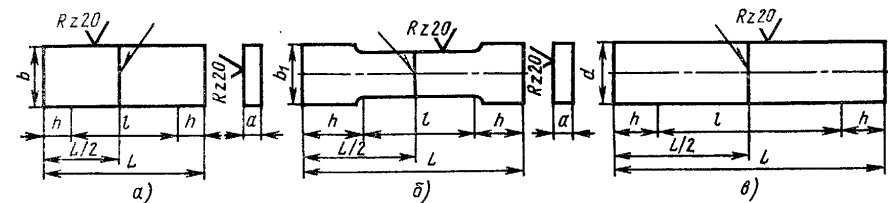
Образцы для определения прочности наиболее слабого участка стыкового соединения при испытаниях сварного соединения на статическое растяжение
